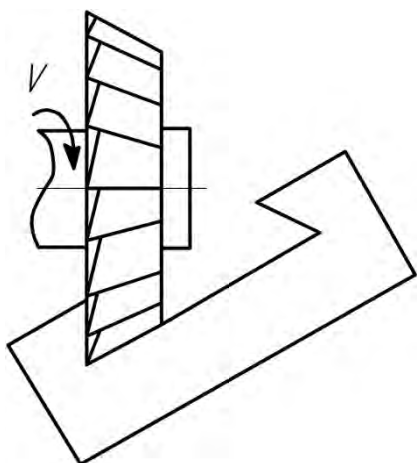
Обработка паза типа «ласточкин хвост» горизонтальным шпинделем дисковой одноугловой фрезой
